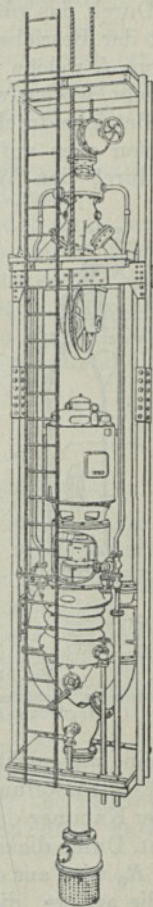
Elektrisch angetriebene Senkpumpe. Gebrüder Sulzer, Winterthur.
